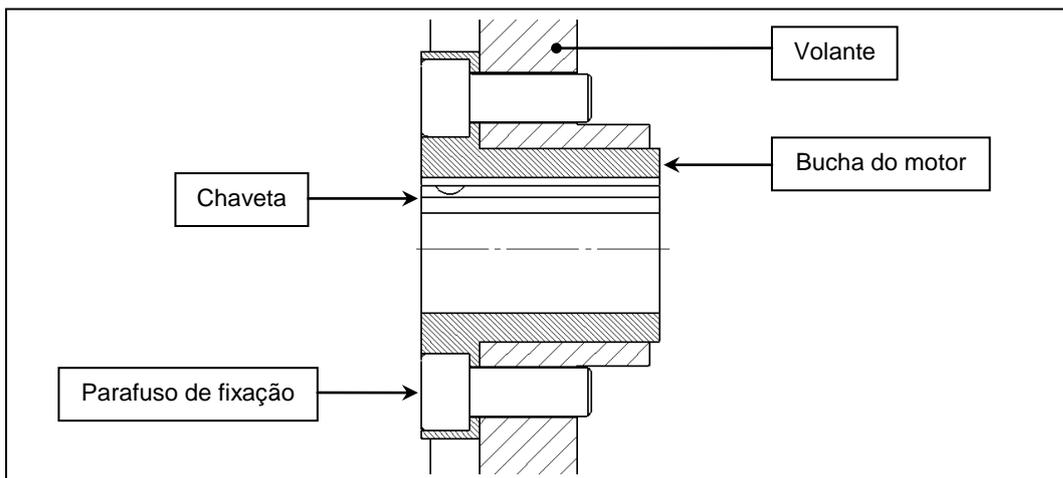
Vista em corte de montagem do volante com a bucha do motor.
